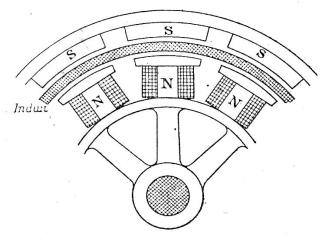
Alternateur volant Ferranti-Patin. Coupe par un plan perpendiculaire à l'arbre.
